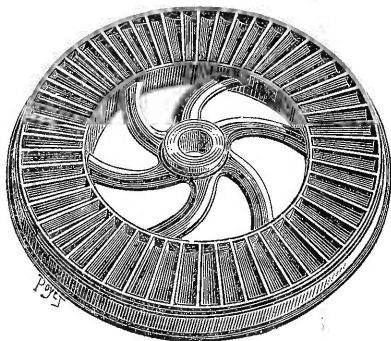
Vue d'ensemble de la roue de la turbine Fontaine.
